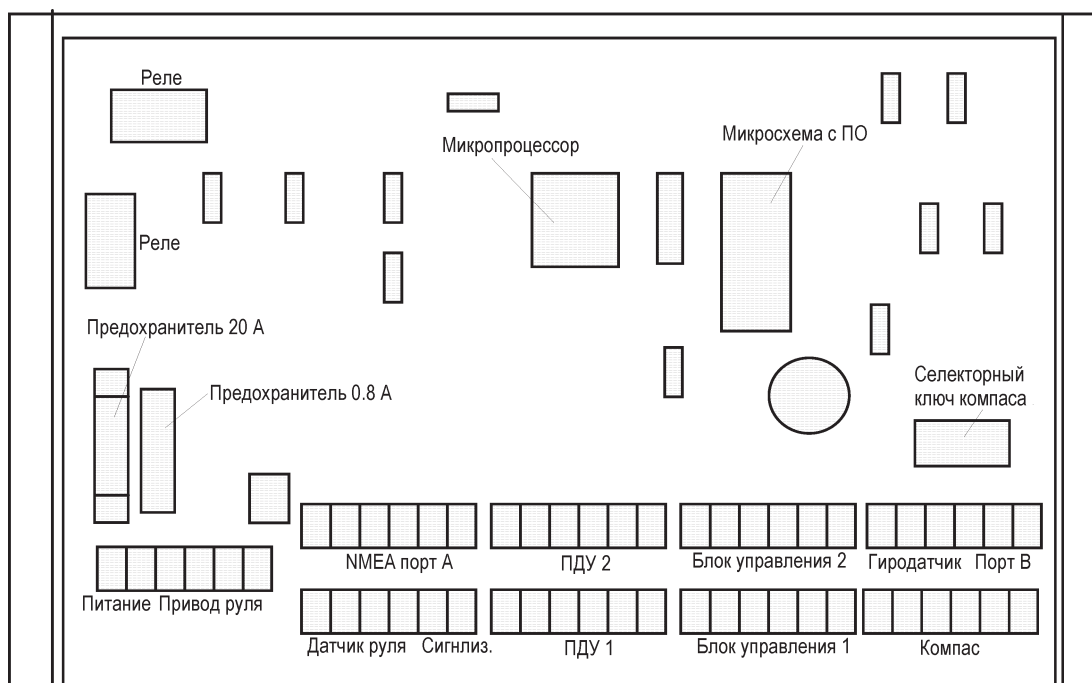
Расположение деталей и разъемов блока курсового процессора CM841
